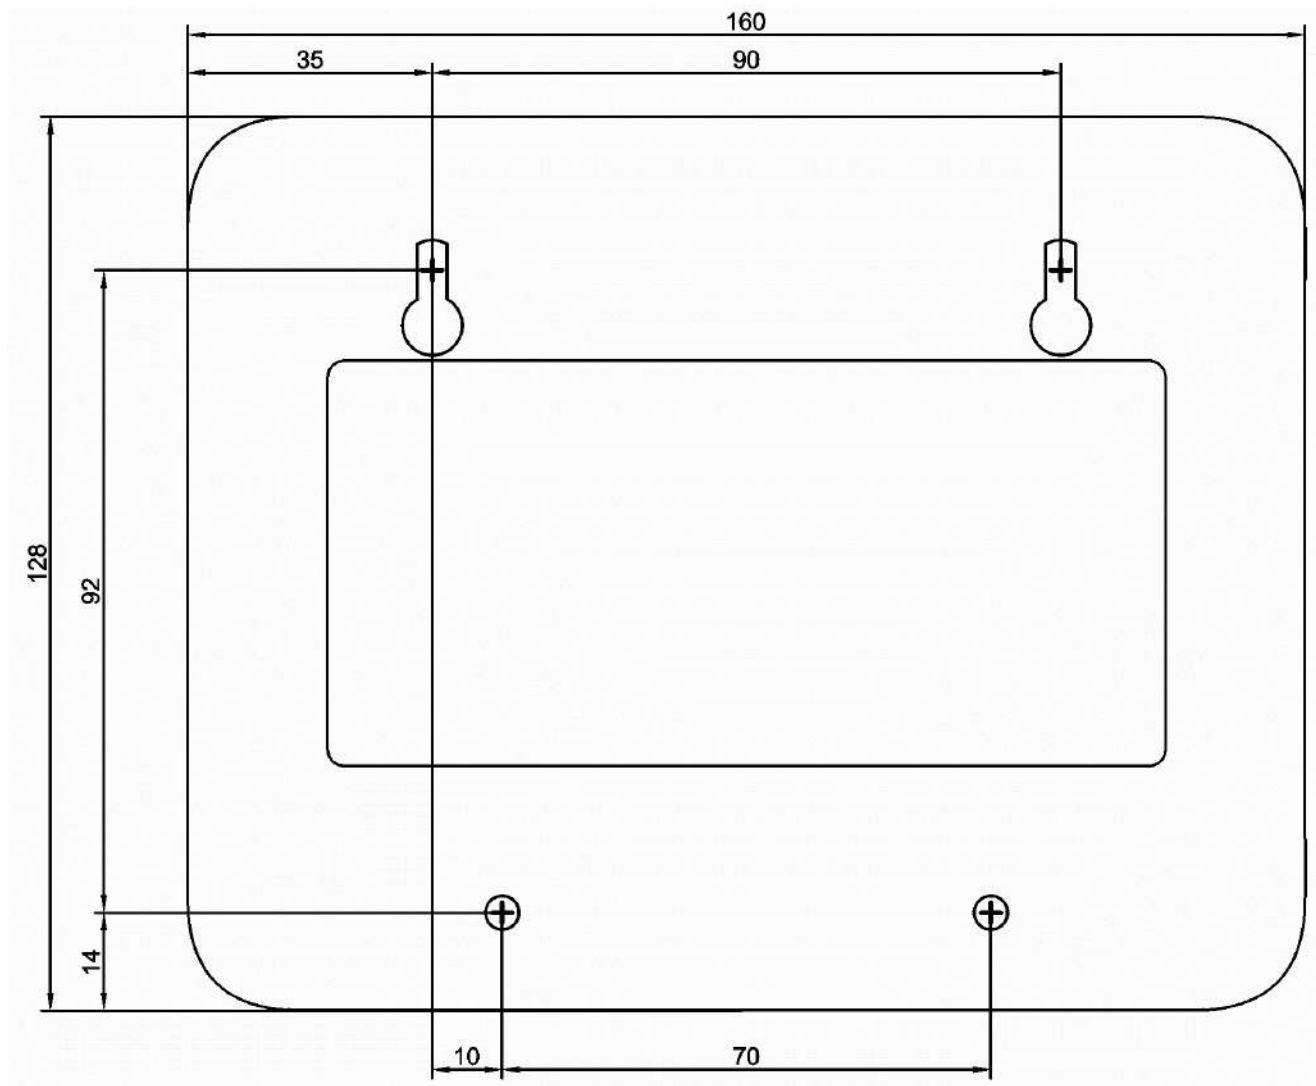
Разметка отверстий для крепления прибора КОП-02.4
